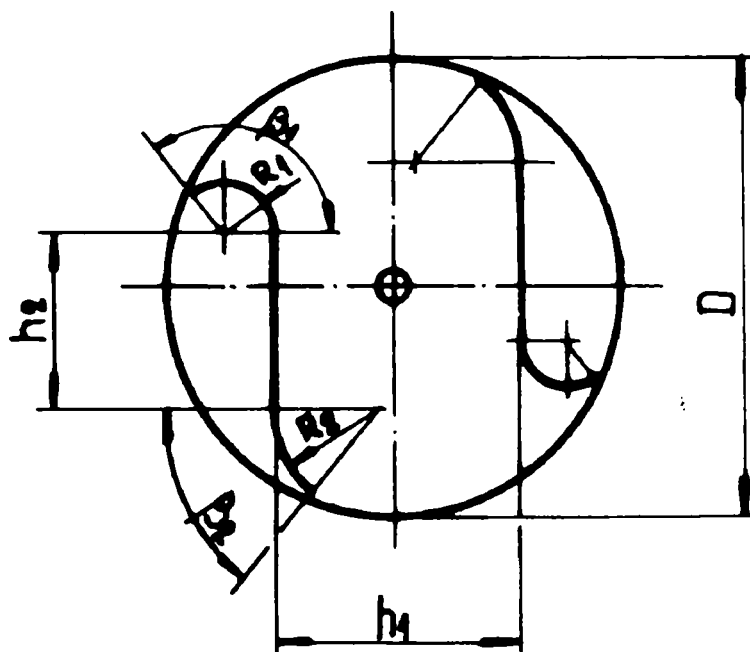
Rotorul cu două pale în formă de S inversat
